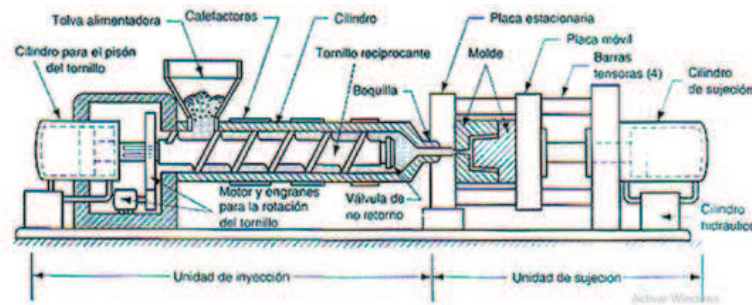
Proceso de fabricación de la Maquina Inyectora.
